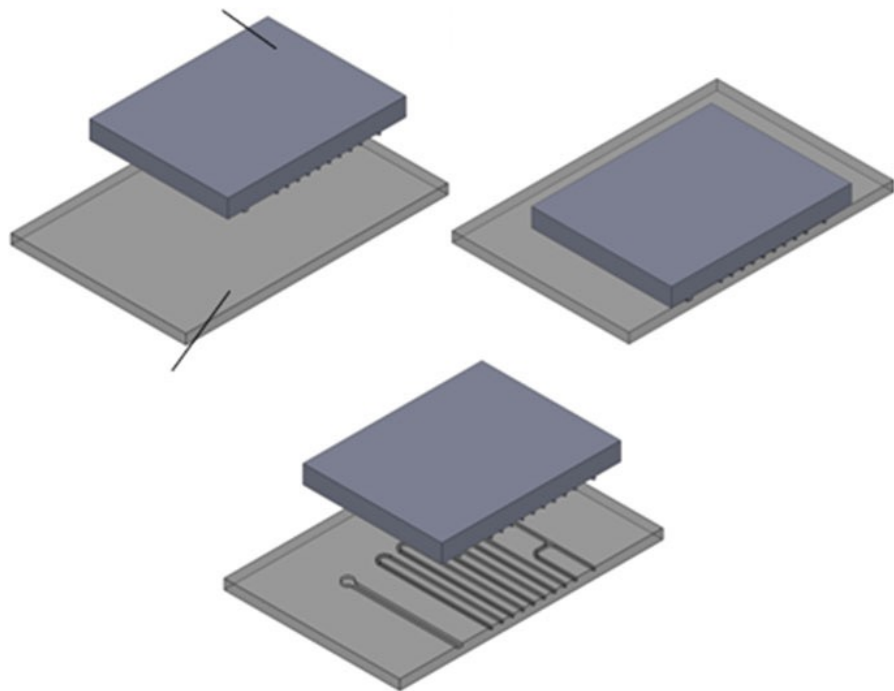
Processo di stampaggio a rilievo a caldo – HE. [15]
